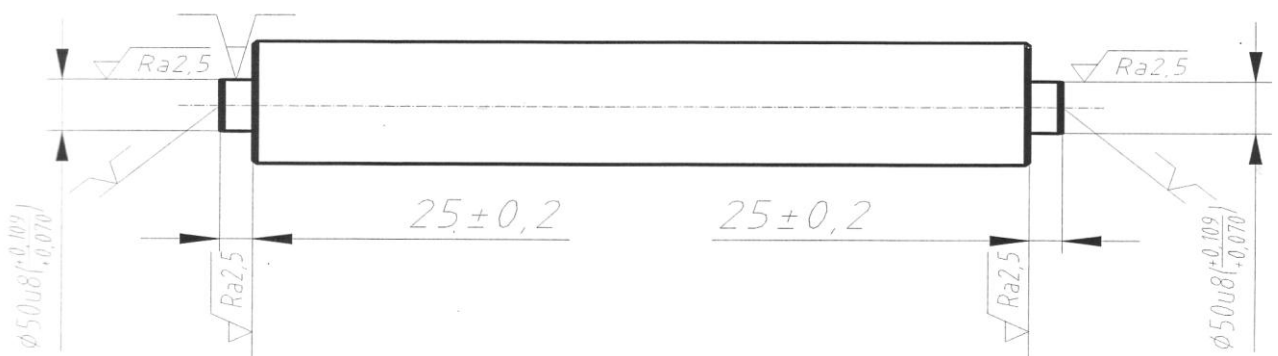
Ескіз обробки деталі операція №090
